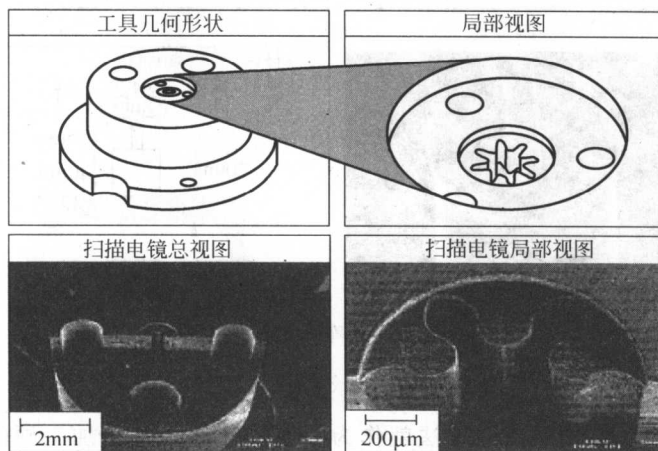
用电火花加工法加工的用于制造微齿轮的模具
